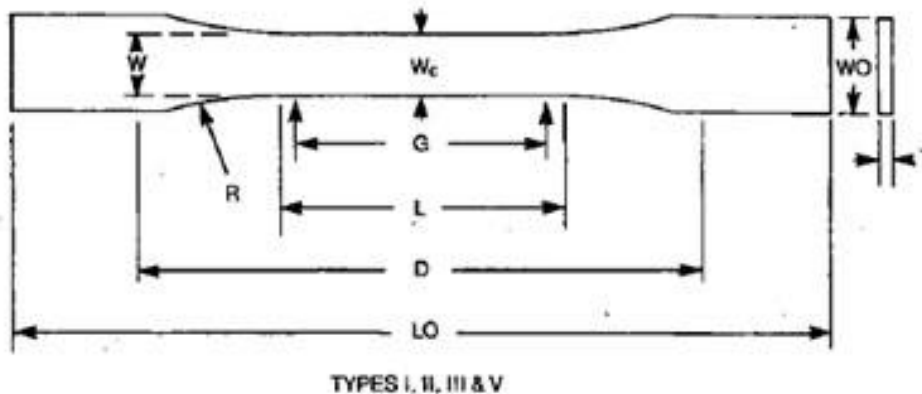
Corpo de Prova Tipo 1 para Ensaio de Tração.
